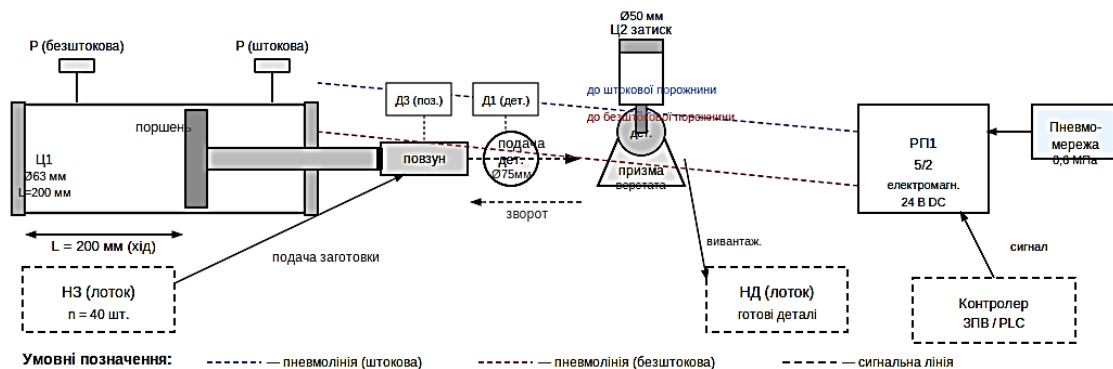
Кінематична схема механізму завантаження (МЗ) з пневматичним приводом: Ц1 — робочий циліндр (Ø63 мм, L = 200 мм); РП1 — пневморозподільник 5/2; Д1 — датчик наявності деталі; Д3 — датчик положення МЗ
